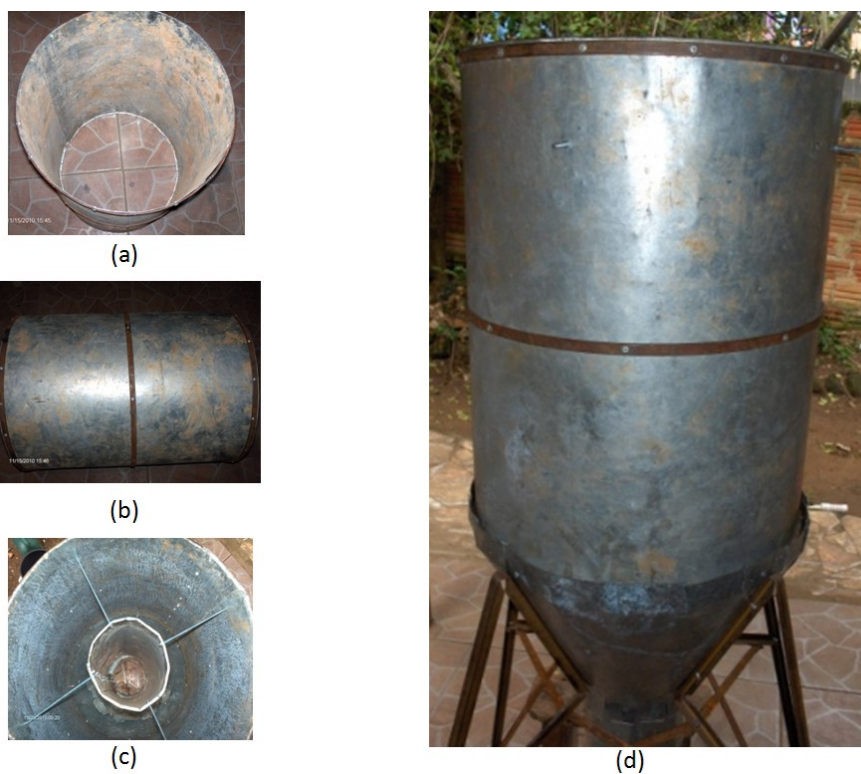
montagem do silo. (a) e (b) construção do cilindro, (c) fixação da parte interna do equipamento e (d) encaixe na base cônica já montada.
